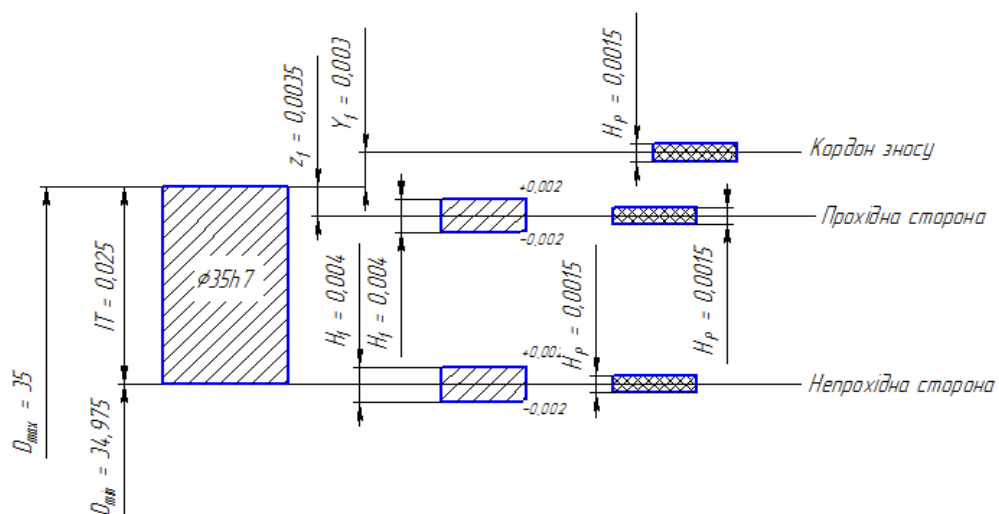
Схема розташування полів допусків калібру-скоби на розмір 35h7
